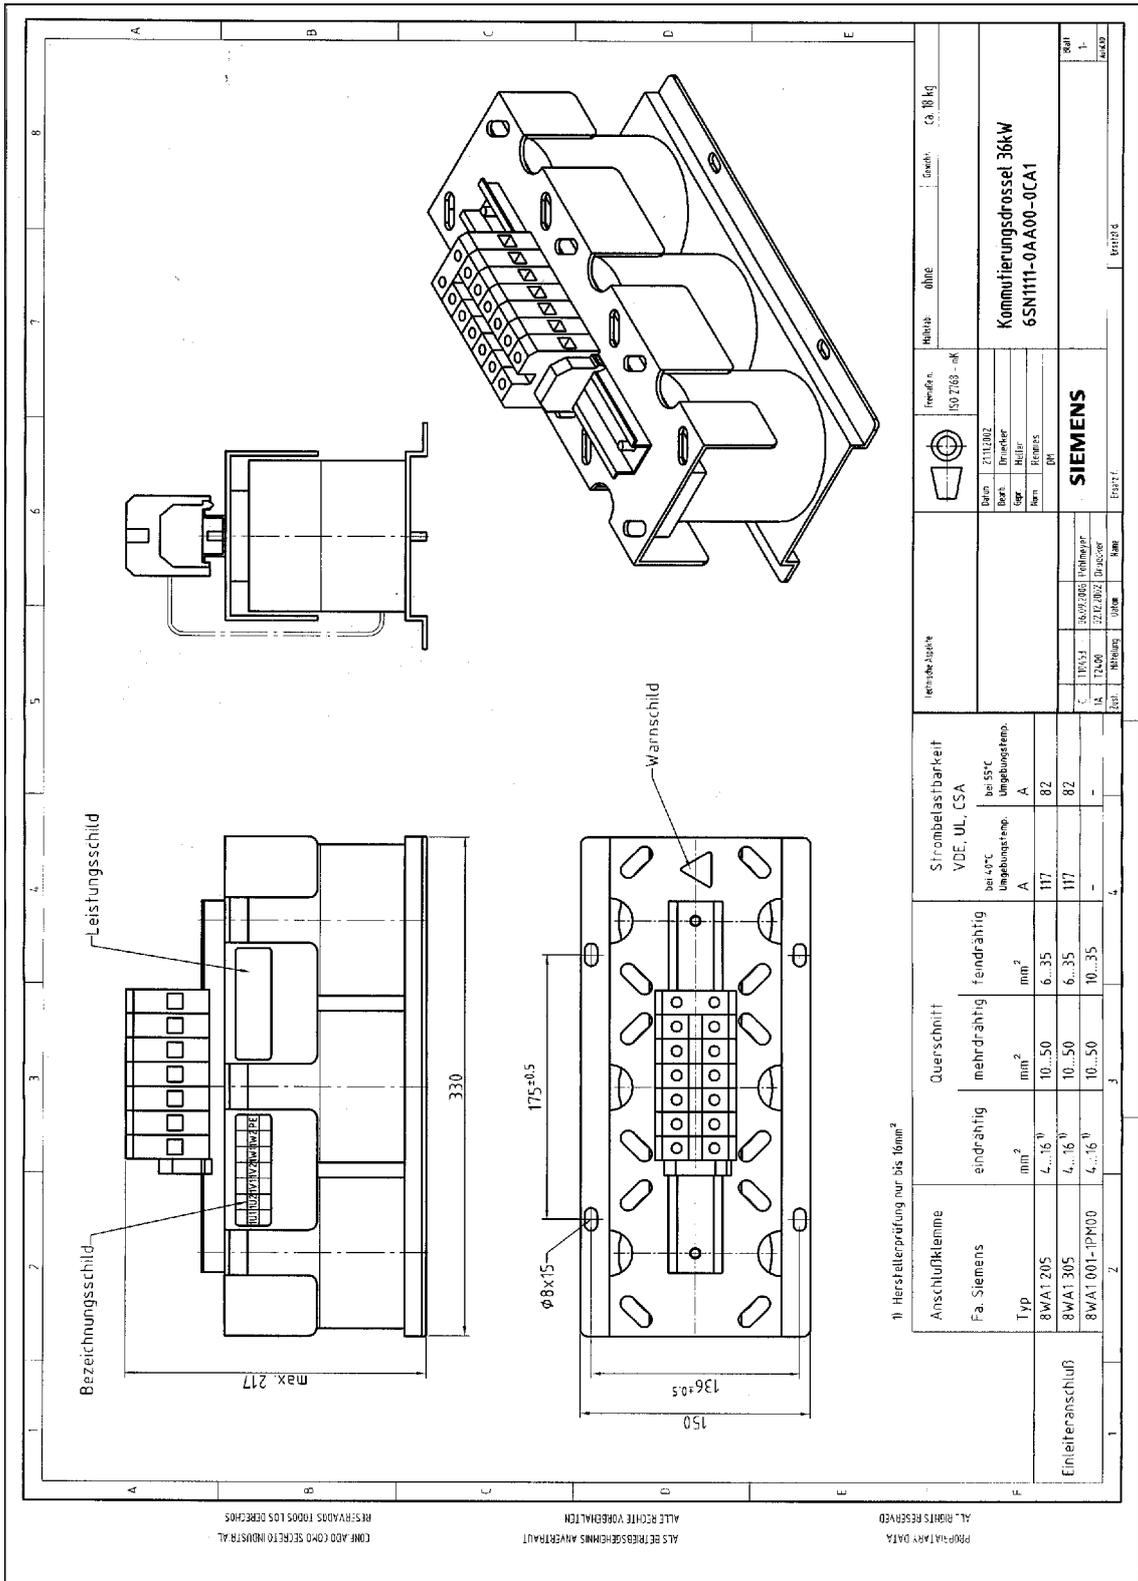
Bobina HF trifásica 36 kW, 6SN1111-0AA00-0CAx
